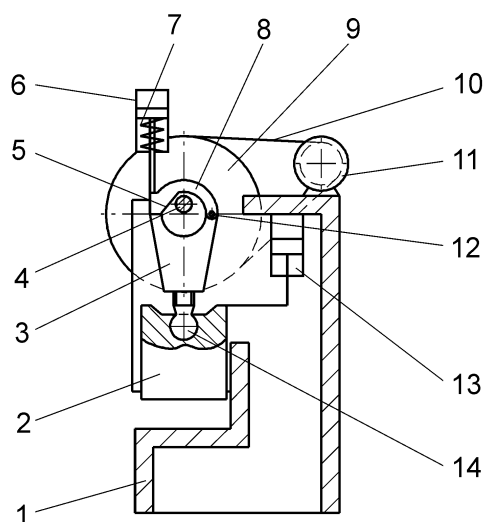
Схема кривошипного пресса с поворотной крышкой шатуна
